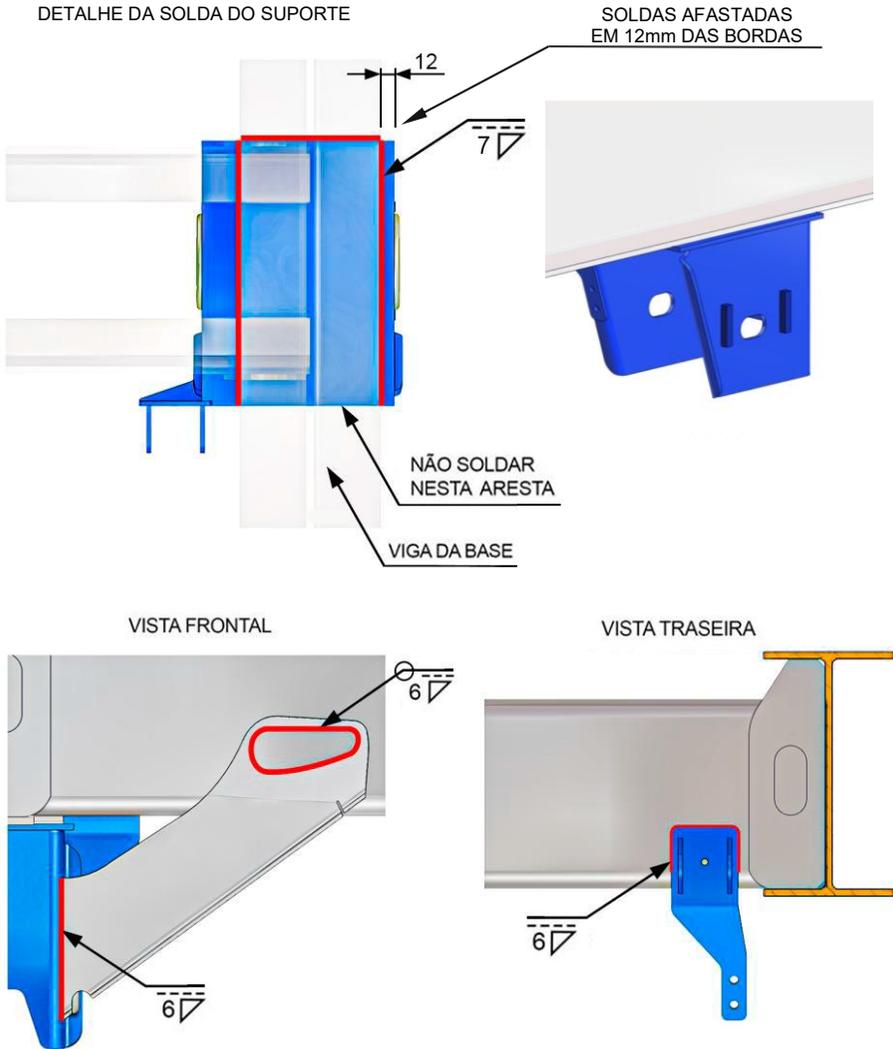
Solda do suporte frontal e reforço de ligação AirSuper H210
